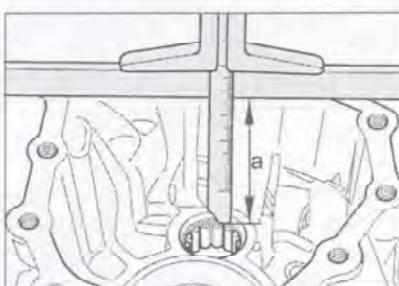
Проверка глубины запрессовки игольчатого подшипника $a = 105$ мм.
